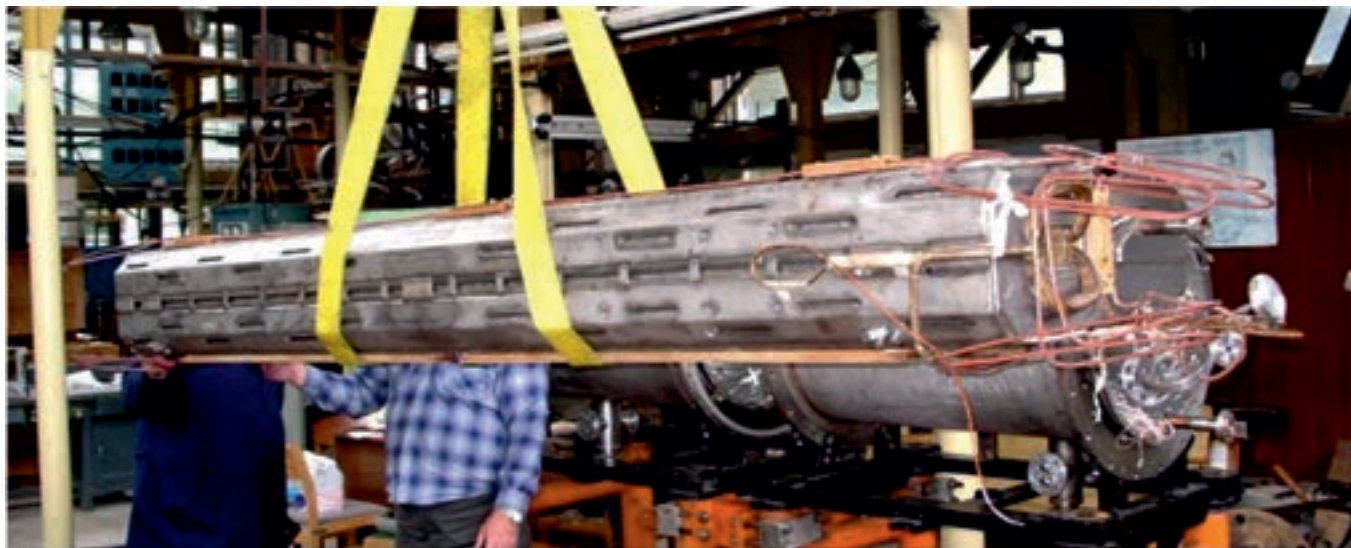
Прототип СП-магнита, изготовленный для FAIR
